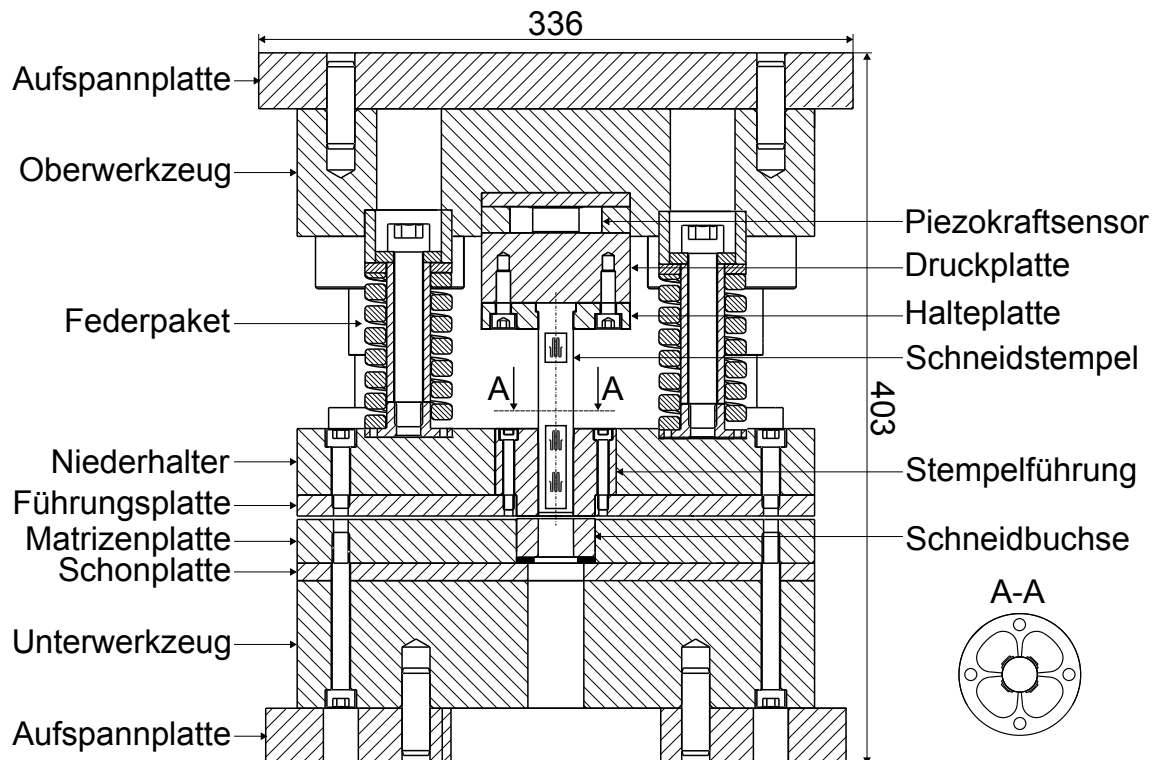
Werkzeug mit Positionen der DMS-Brücken und Aussparung in der Führung
